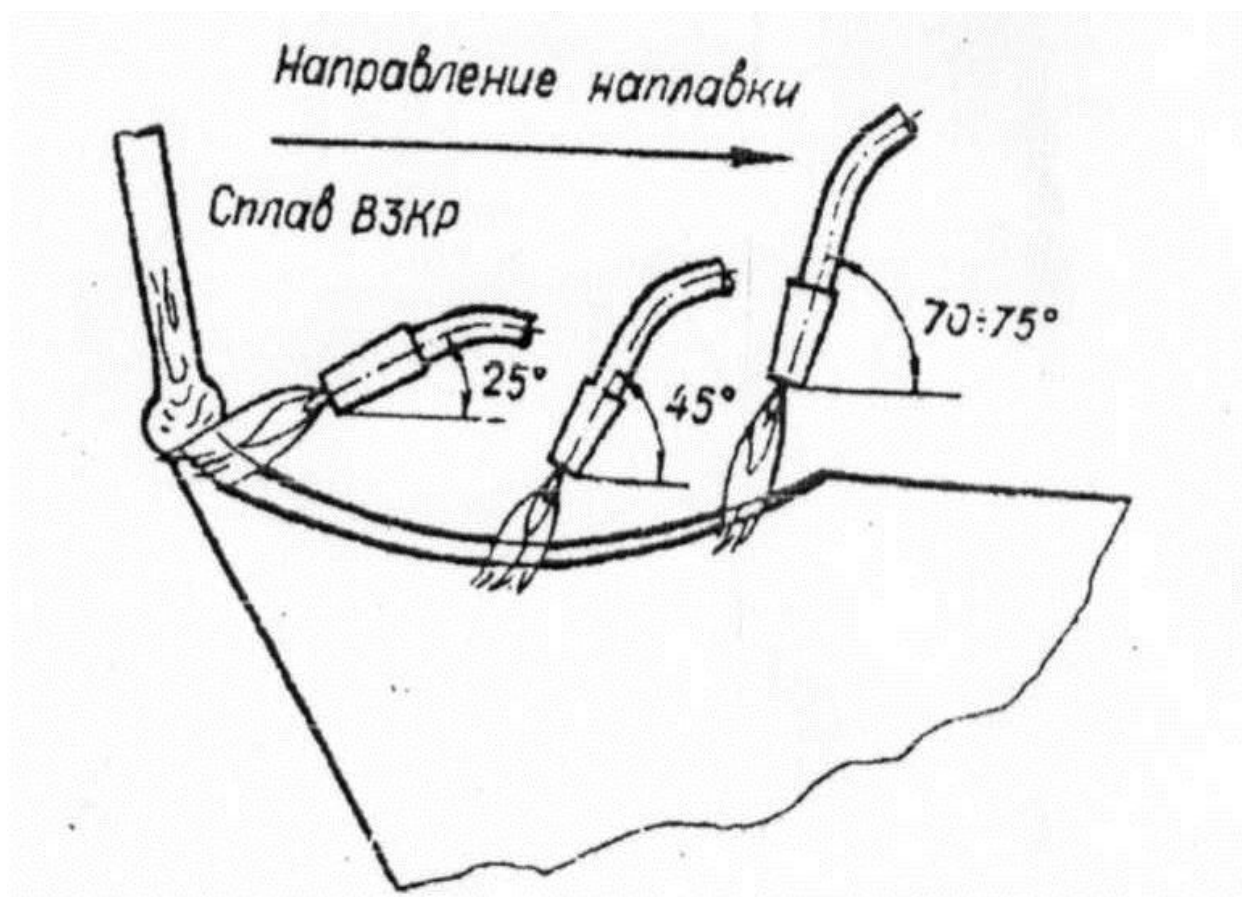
Положение прутка стеллита и наконечника горелки при наплавке
